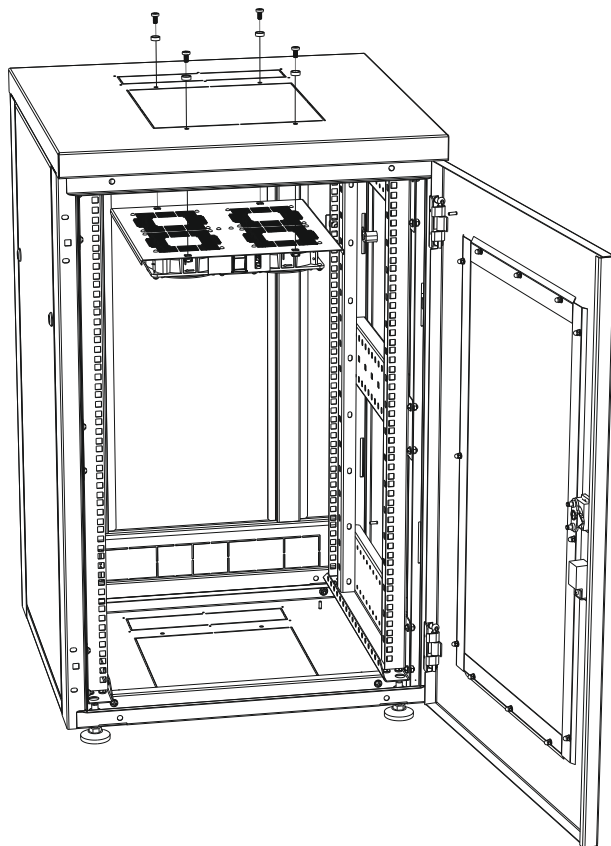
Установка вентиляторного блока в крышу напольного шкафа TFI-R
